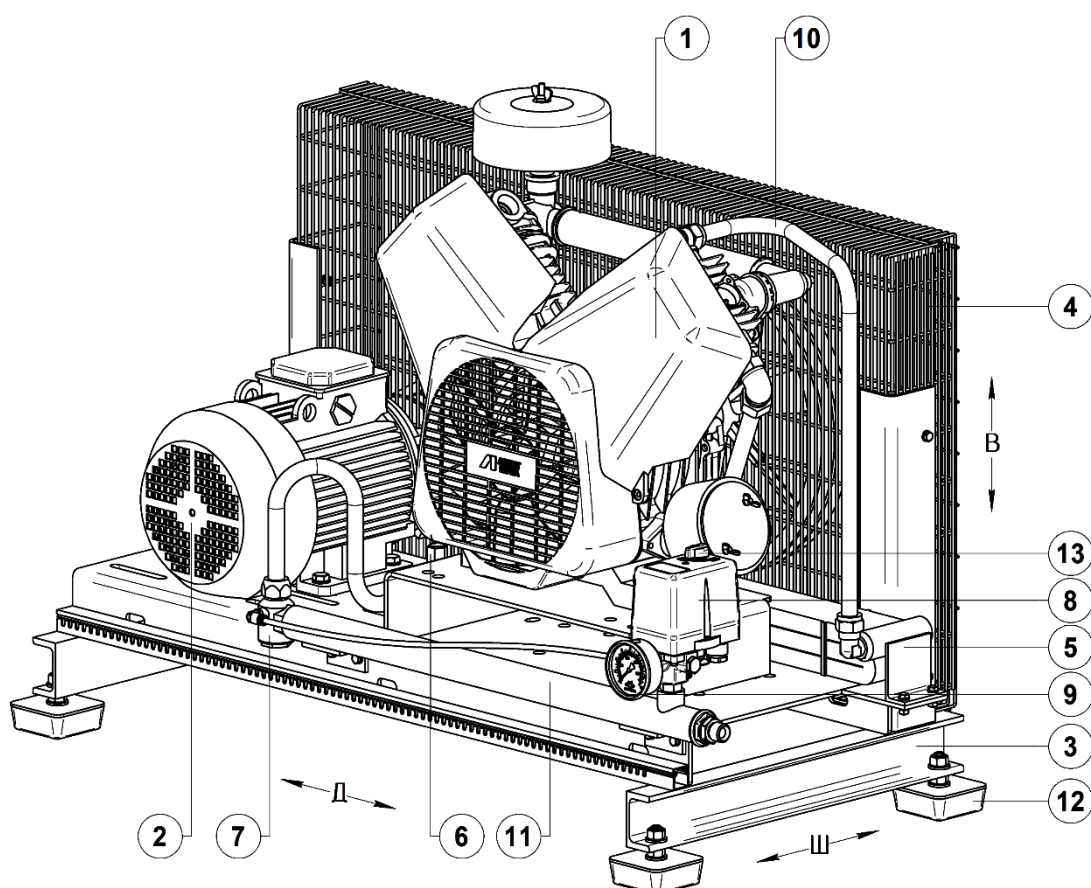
Общий вид компрессора СБ4-ФЗ7
